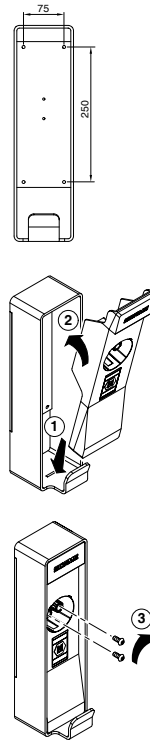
INSTALLATIONSBEREICH DES STECKERHALTERS
